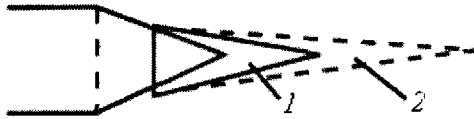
Оптимальный вид пламени горелки для пайки твердым припоем:
